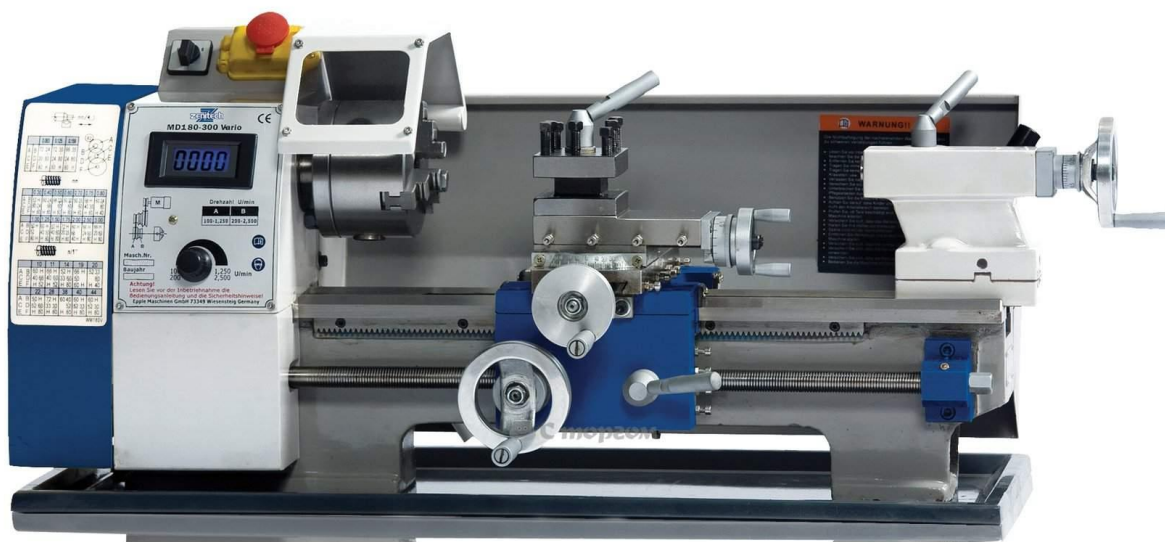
Сучасний токарний верстат з обробки металу
